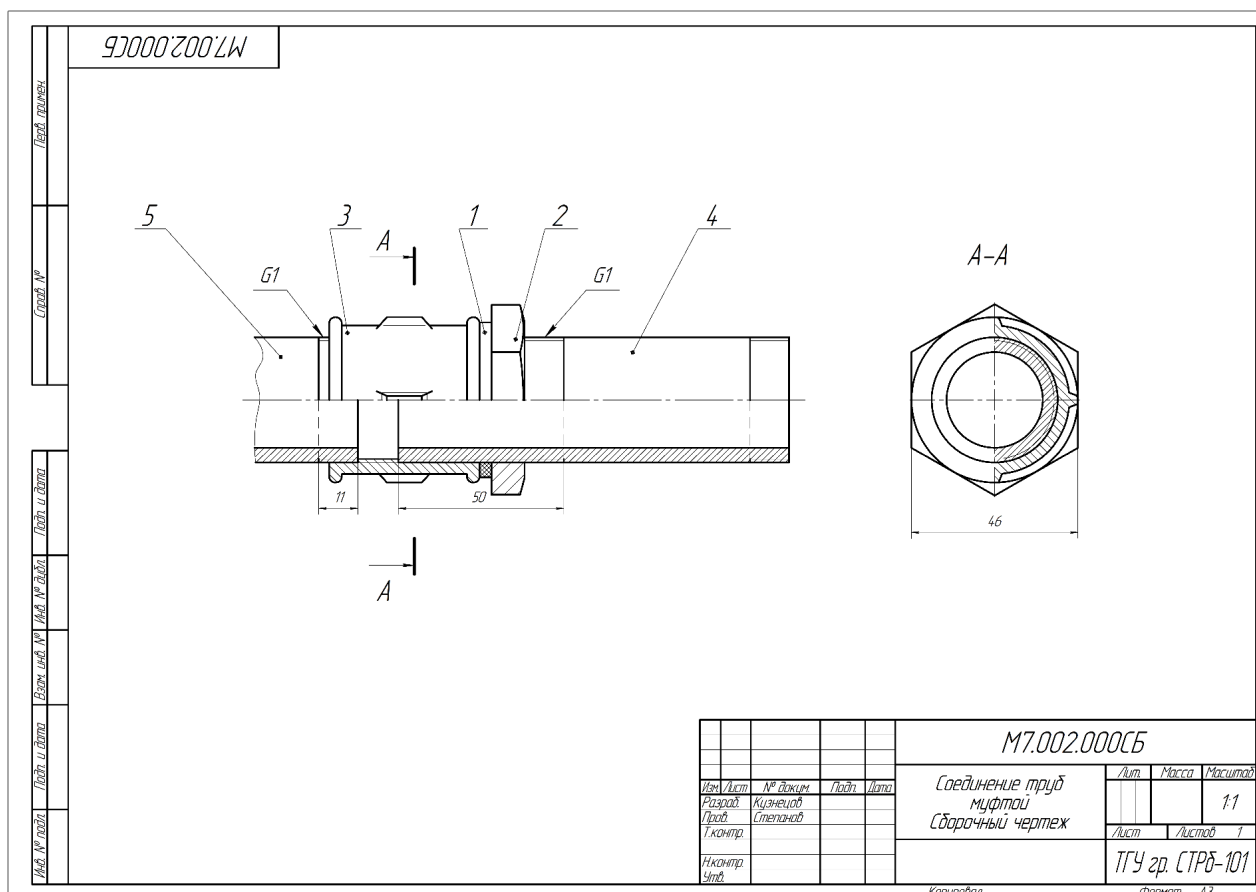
Пример выполнения сборочного чертежа трубного соединения
